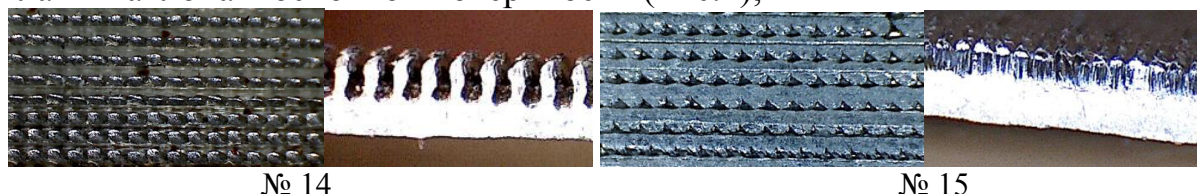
Характерный вид сверху и поперечный срез образцов поверхностей кипения с трехмерным рельефом. Обозначения и параметры образцов представлены в Табл. 2.
